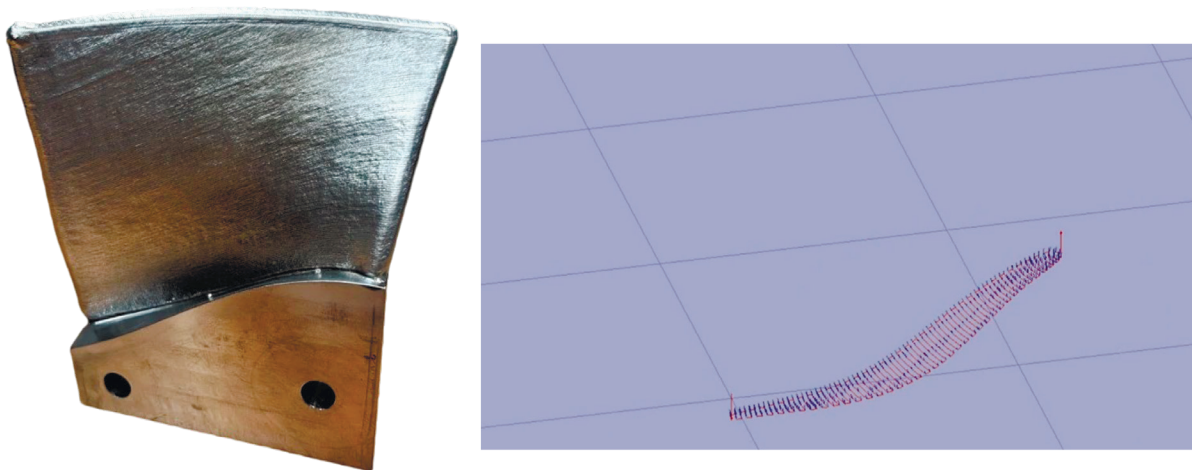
Пример ремонтной наплавки лопатки компрессора из сплава ВТ6 с использованием непланарного слайсинга
